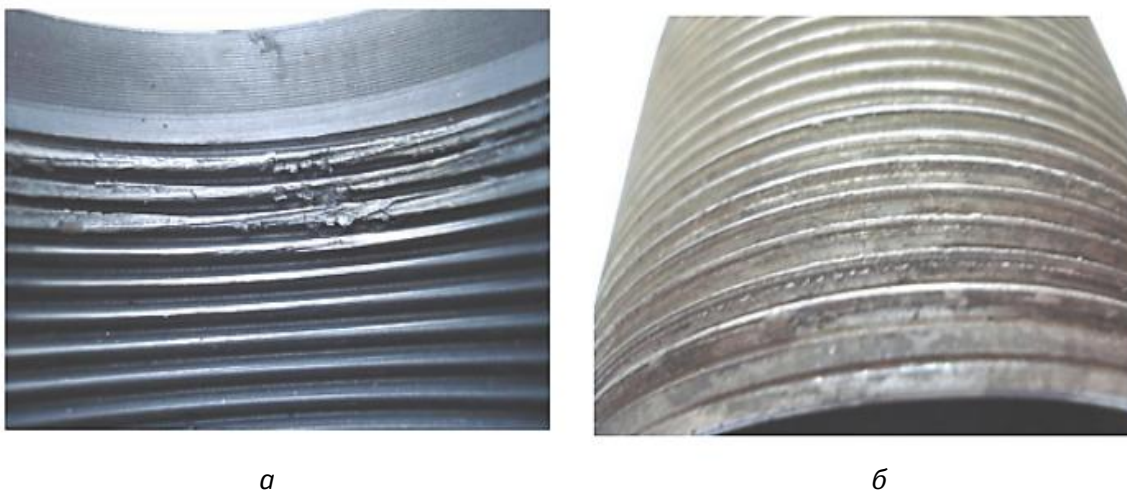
Смятие на первых витках резьбы корпуса (а), основания или головке (б)
